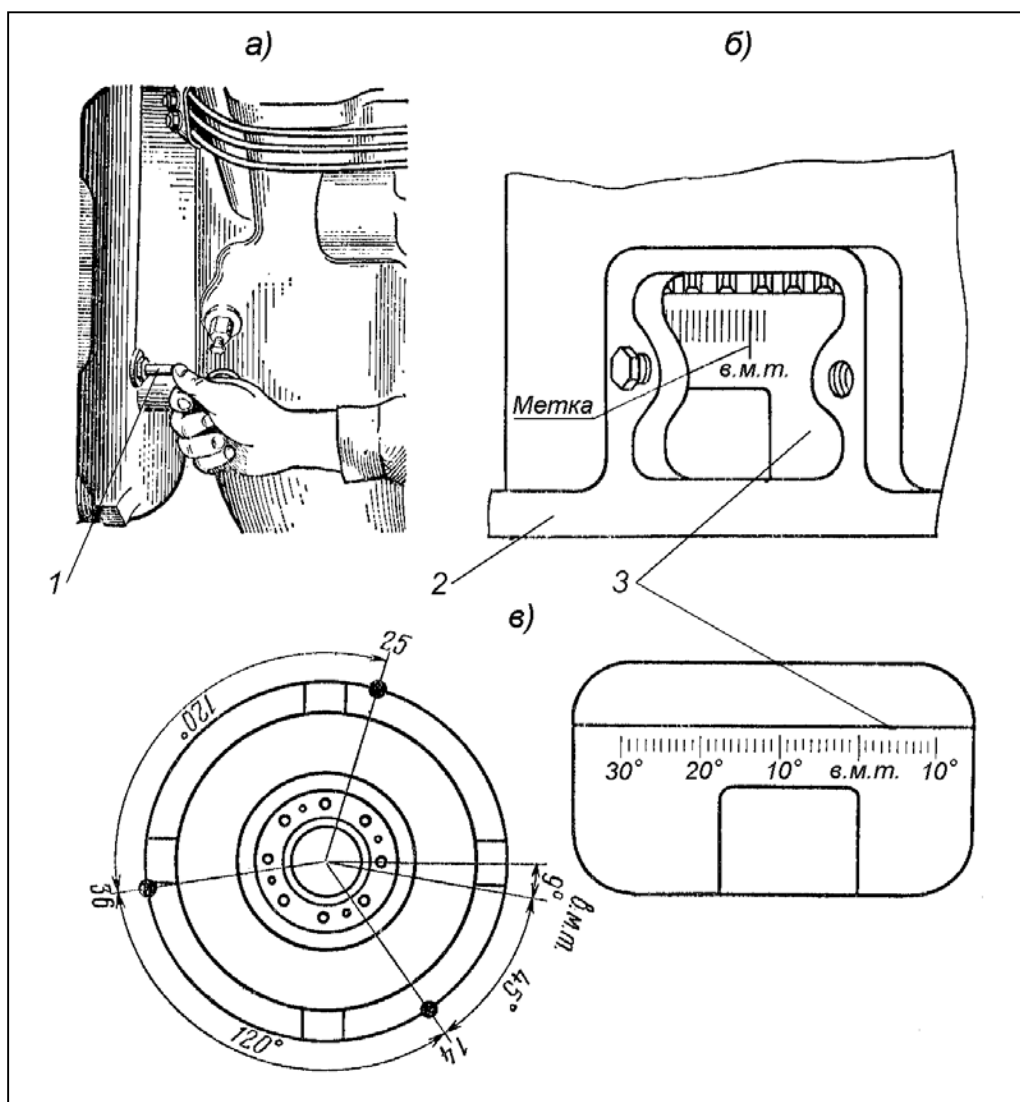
К установке коленчатого вала двигателей СМД-60...СМД-73 при регулировке клапанов:
